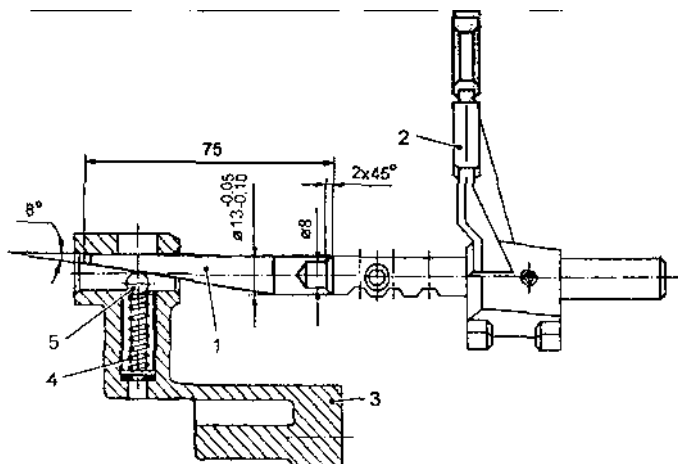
Установка штоков с вилками включения передач в корпус механизма переключения передач:
